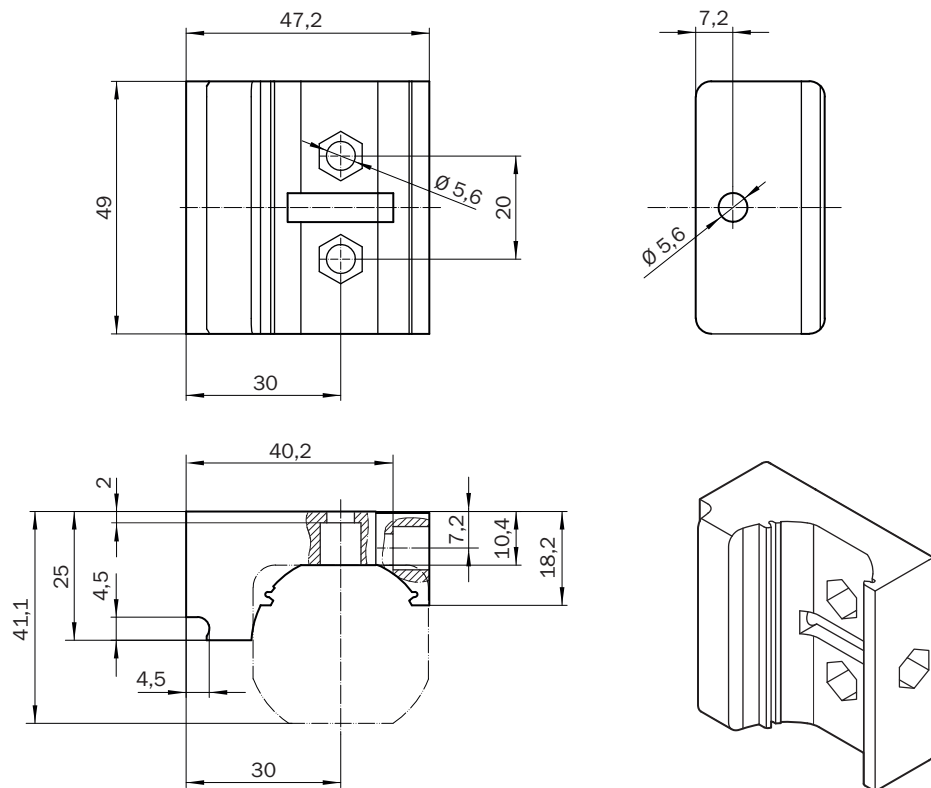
Габаритный чертеж крепления QuickFix (2066048)
